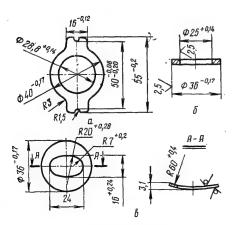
Пластины и пружины клапанов крупных компрессоров:
